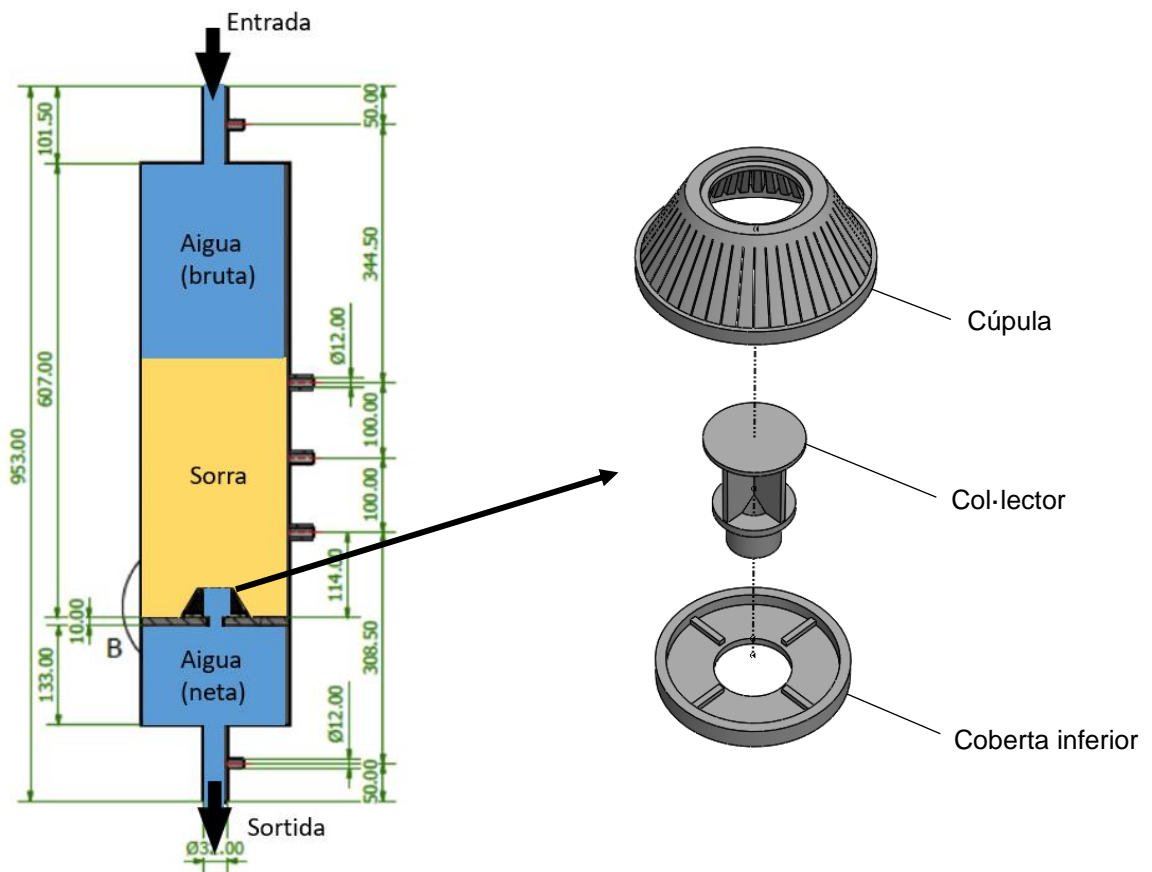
Esquema del filtre a escala amb la vista explosionada de la crepina (dimensions en mm)
